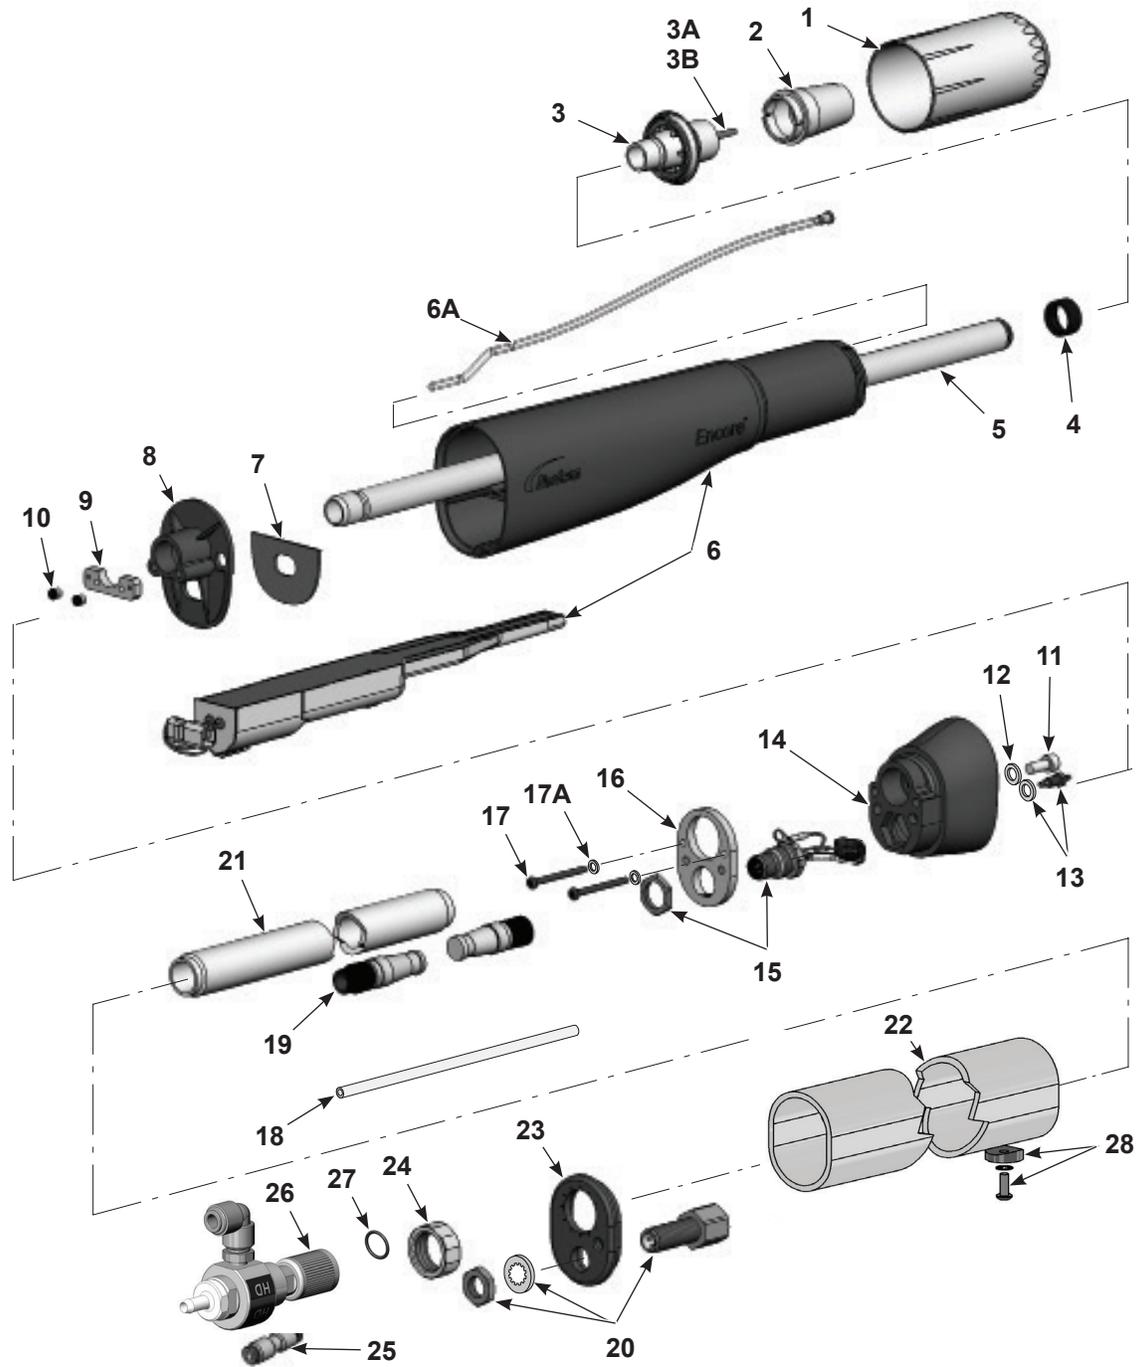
Piezas de repuesto de una pistola de aplicación de montaje en tubo
